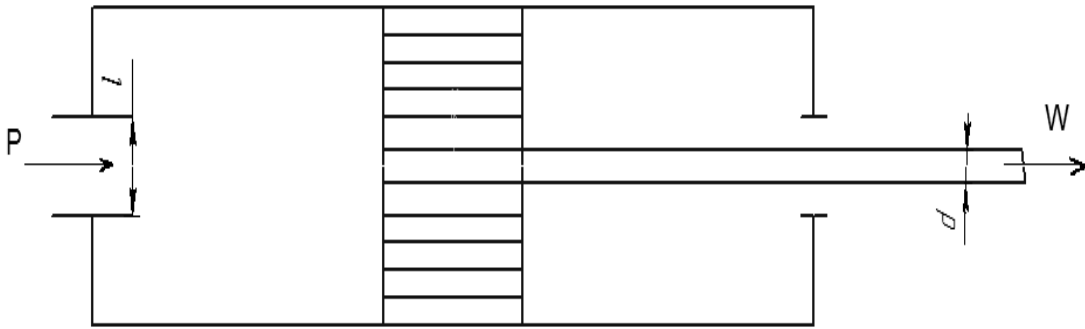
Розрахункова схема пневмоциліндра
